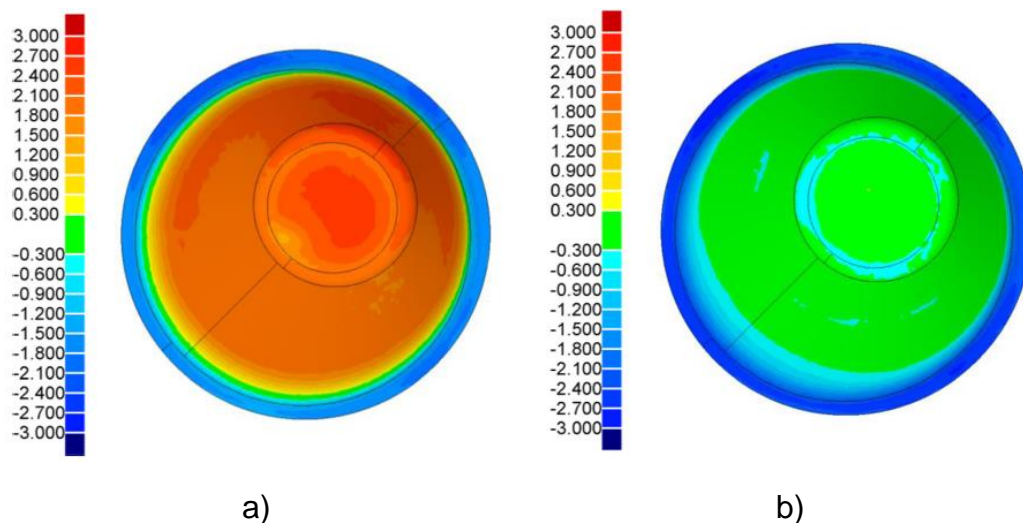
Desviaciones geométricas de una pieza asimétrica de AA 7075-O fabricada mediante SPIF a) sin y b) con control MPC [Lu, 2017-a].
